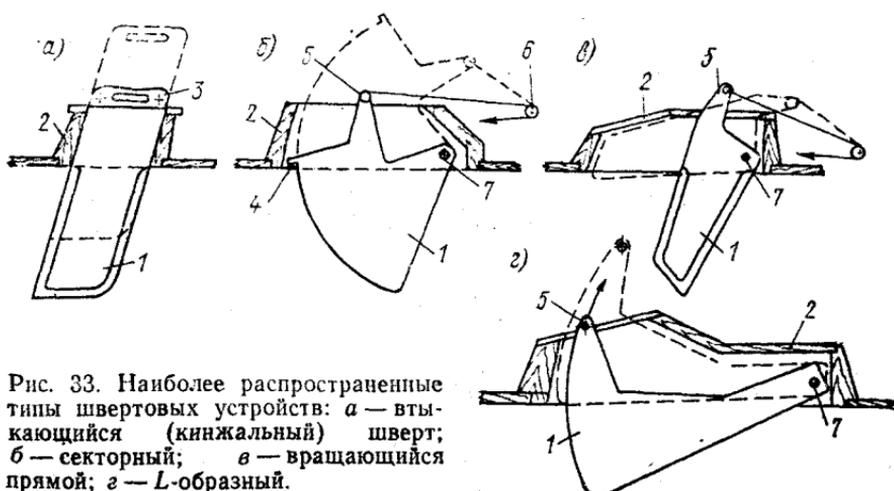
Наиболее распространенные типы швертовых устройств: а — втыкающийся (кинжальный) шверт; б — секторный; в — вращающийся прямой; г — L-образный.
